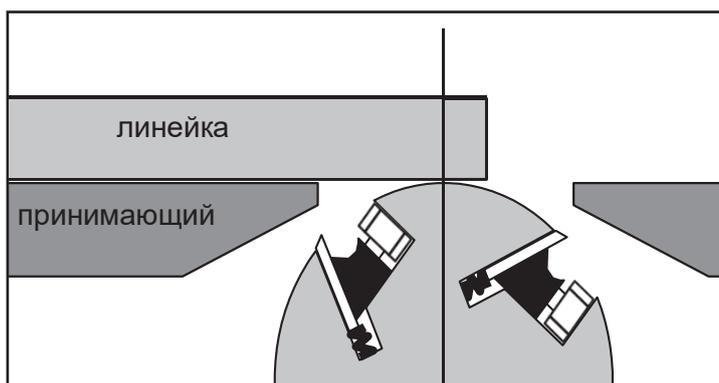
Регулировка отводящего стола даже с корпусом режущего вала (показан режущий вал с ножами).
